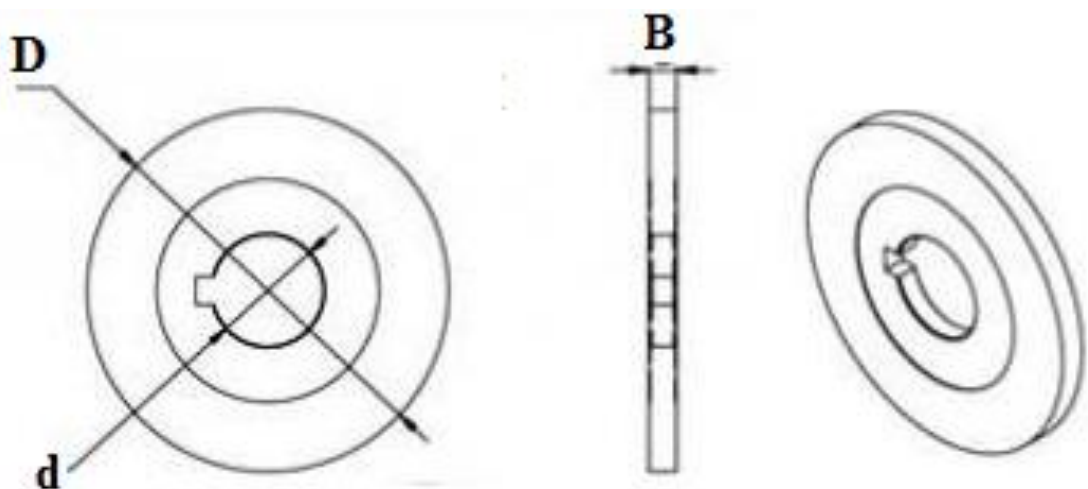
Основные размеры дисковых ножей по металлу
